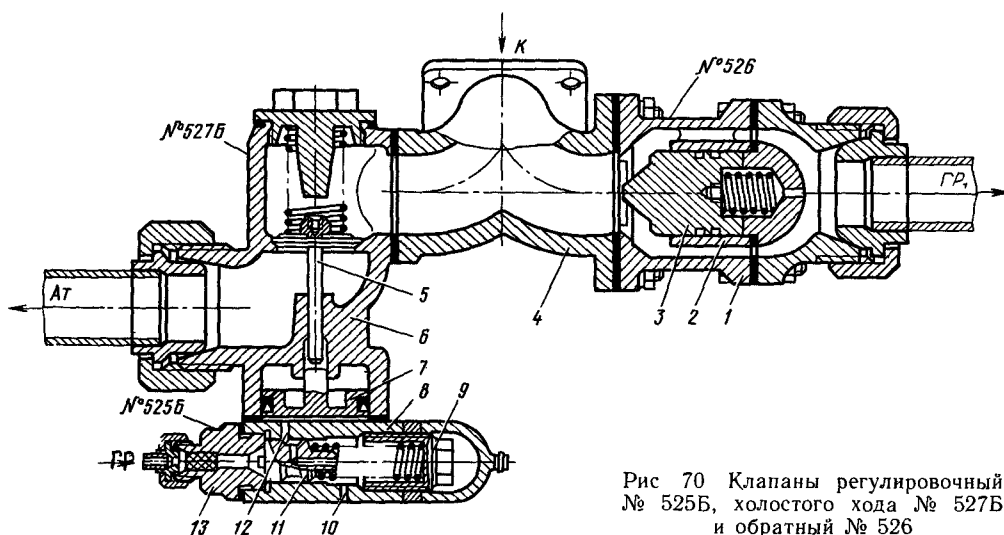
Клапаны регулировочный № 525Б, холостого хода № 527Б и обратный № 526
